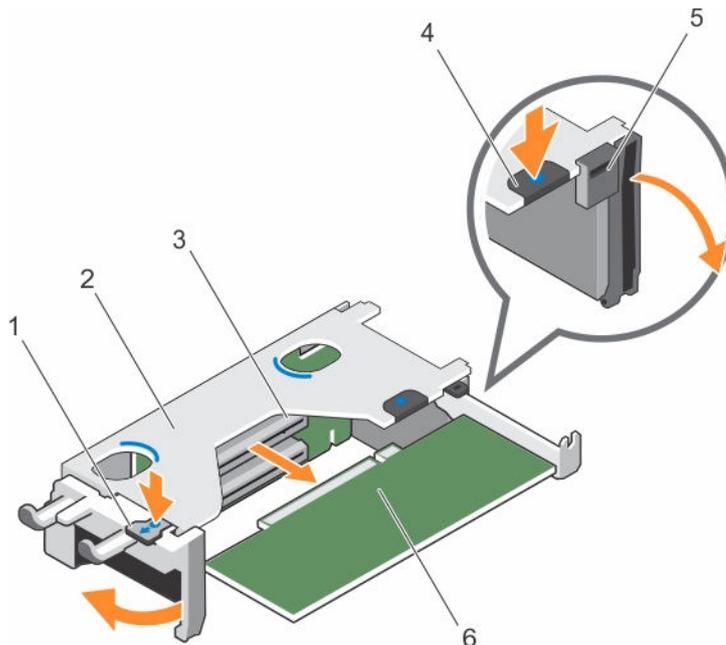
Remover uma placa de expansão da riser de placa de expansão 1
